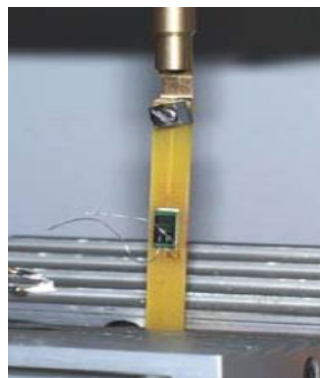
Místa utržení při testu stříhem dle [22].
